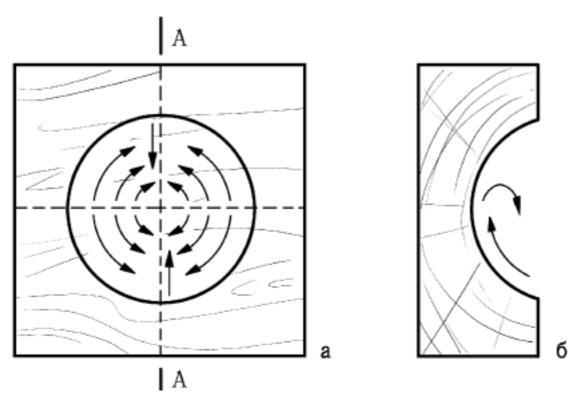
Выполнение резьбы вогнутой выемки на пласти заготовки первым способом (стрелками показано направление движения инструмента): a – вид сверху;  $\delta$  – вид сбоку
